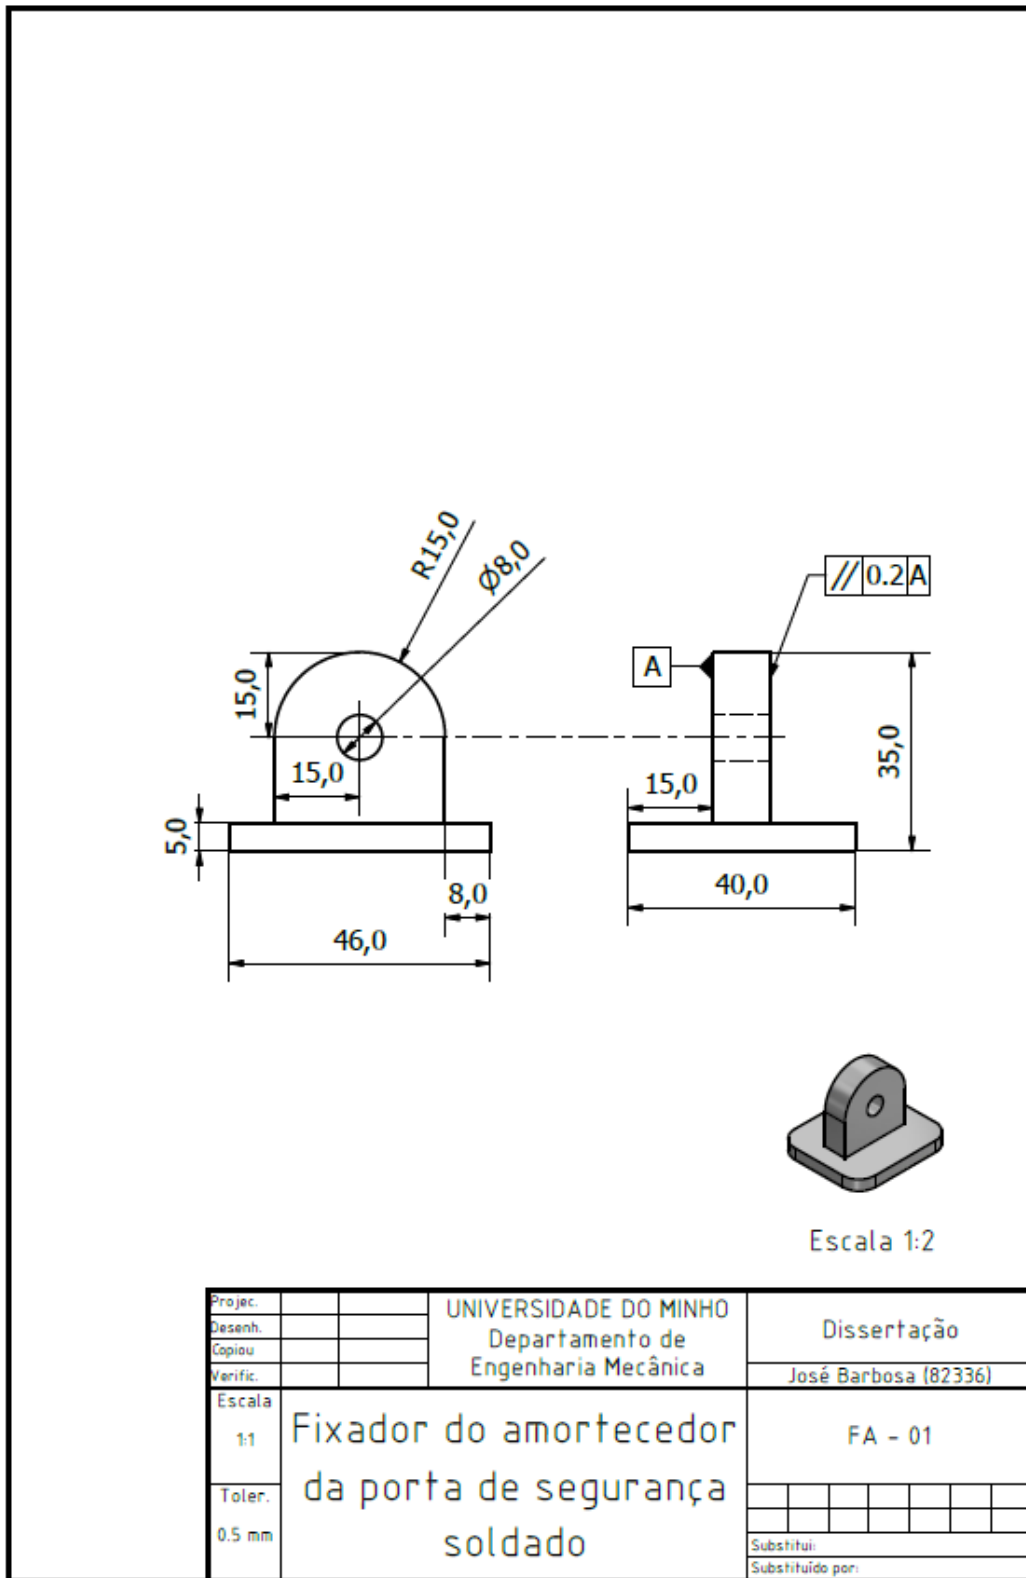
Figura Anexo III-35 – Desenho técnico do fixador do amortecedor da porta de segurança soldado.
